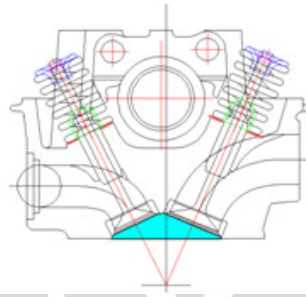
Proses OP 130 *Cylinder Head Machining
